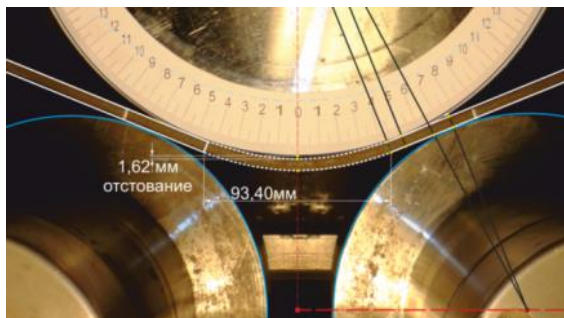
Отрыв заготовки от деформирующего инструмента в зоне очага деформации
